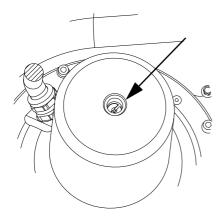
Вал электродвигателя в разрезе, вид сверху
